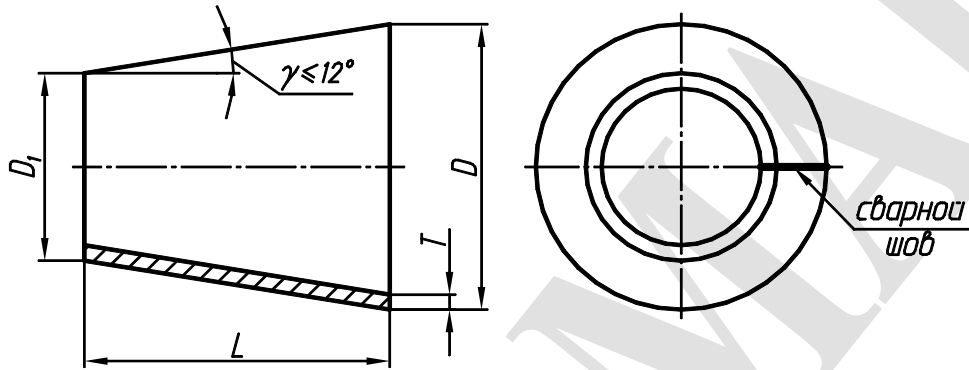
Конструкция и основные размеры перехода сварного
